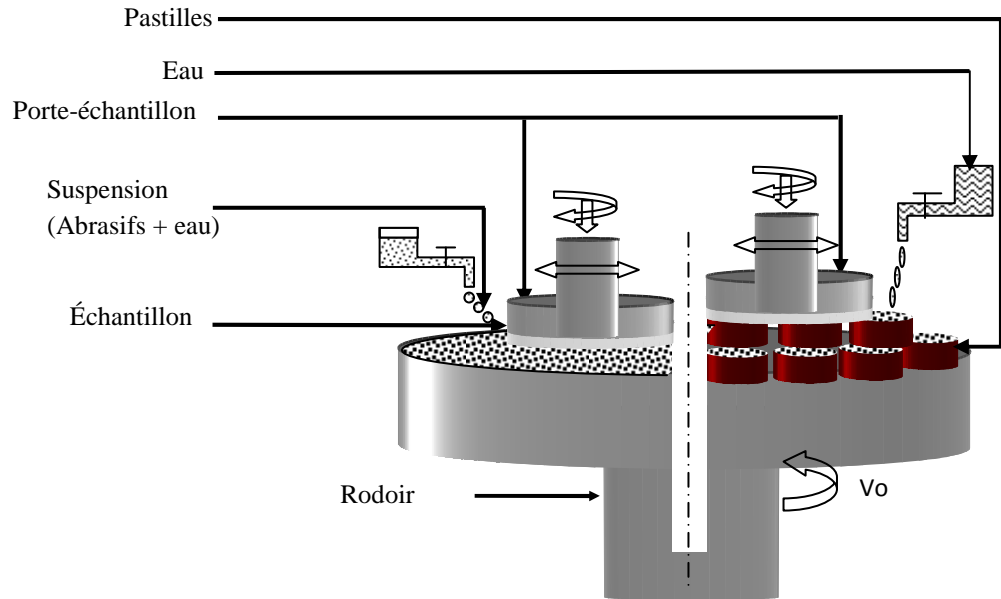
Principe de rodage par abrasif en suspension et par pastille.
